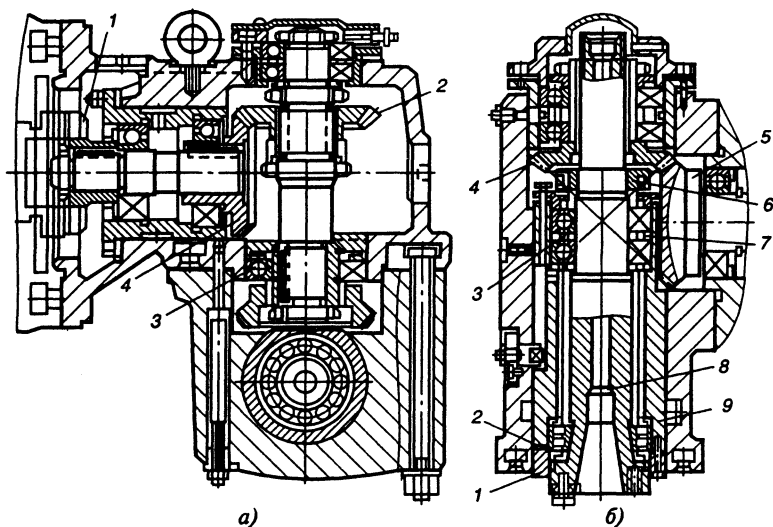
Поворотная головка (а) и разрез по шпинделю поворотной головки (б)
